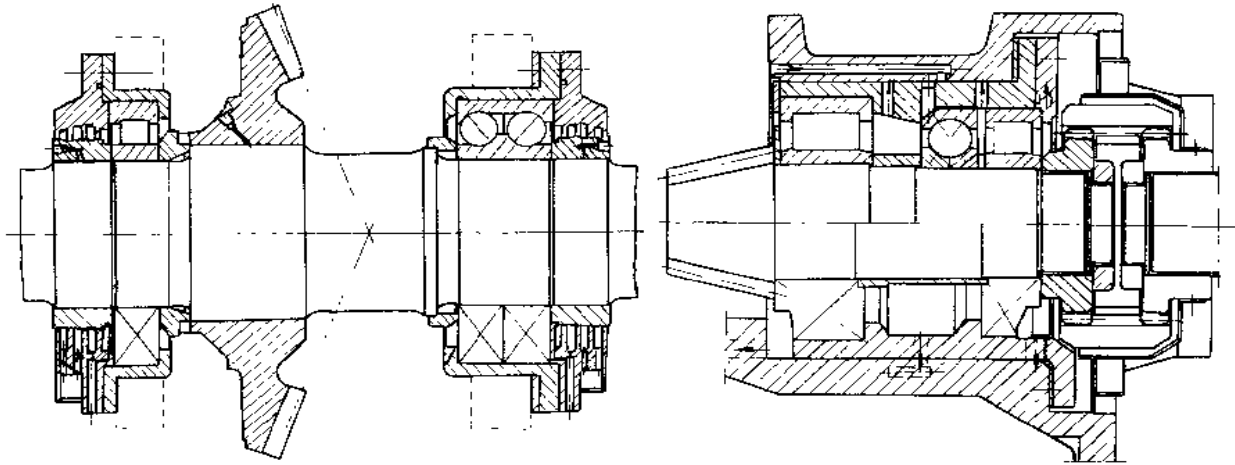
驱动轴装配一套圆筒形滚柱轴承
